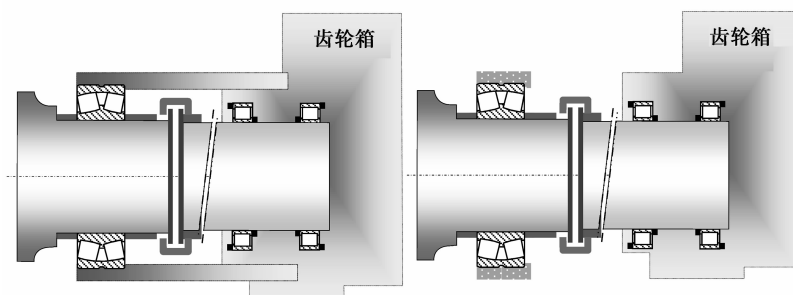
三点支承: 主轴轴承 + 齿轮箱中的轴承
